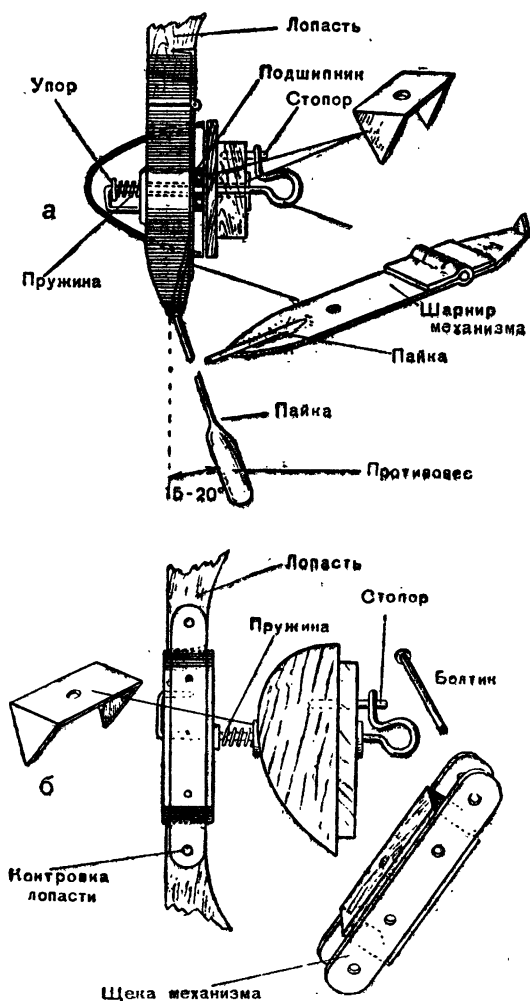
Конструкции складывающихся лопастей воздушного винта.
